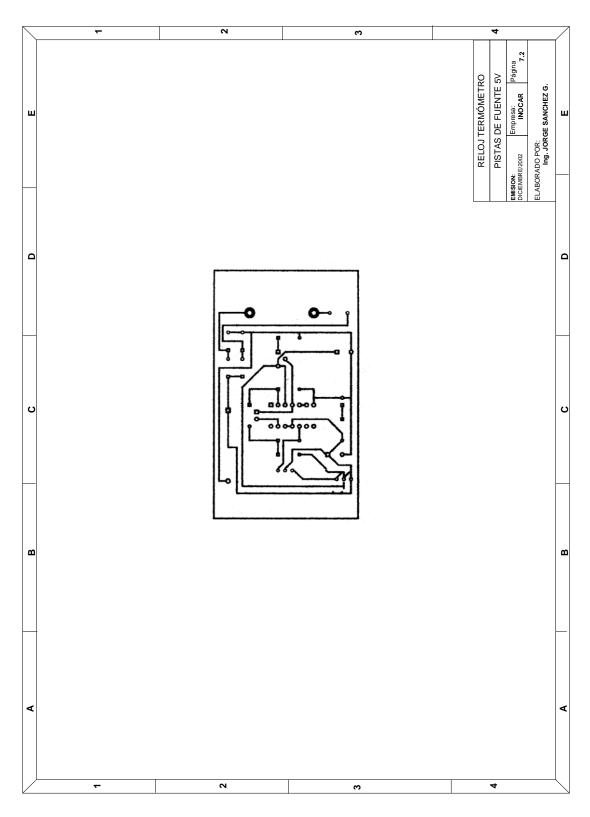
Tarjeta de fuente 5VDC (Diagrama de pistas lado de soldadura)
